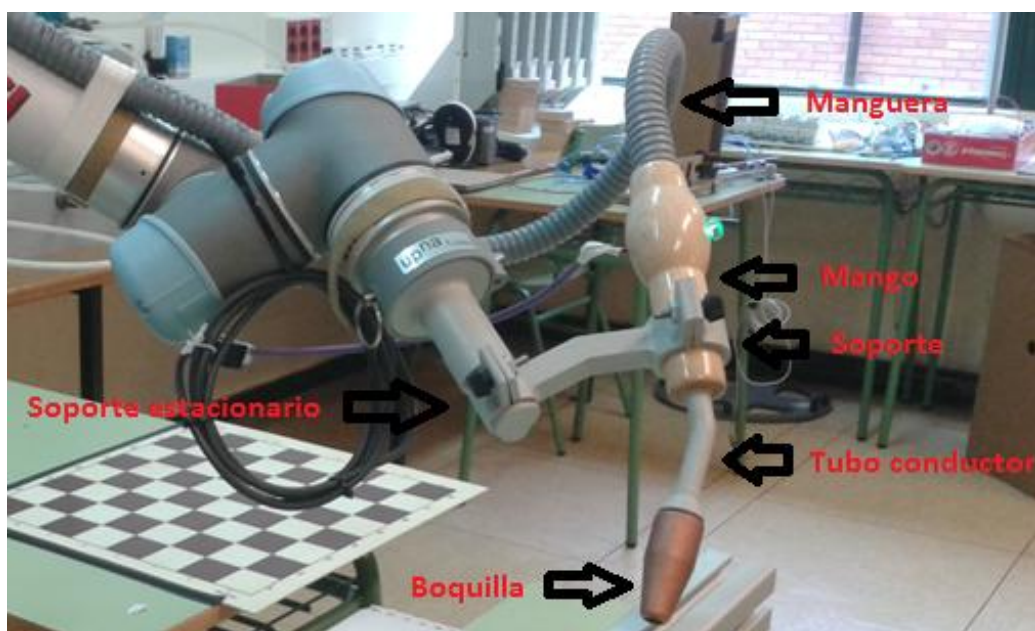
Componentes del diseño de la pistola de soldadura
